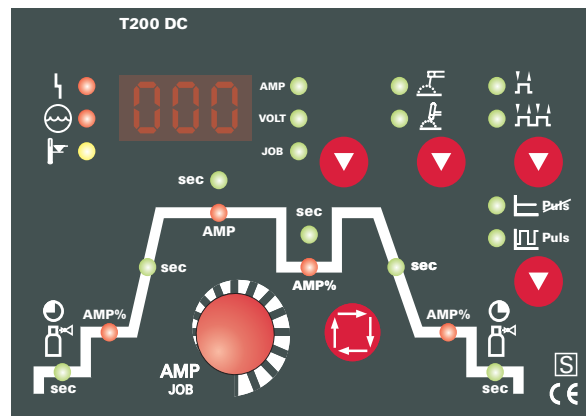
Устройство управления инверторного источника тока EWM для сварки ВИГ TRITON 220 DC PowerSinus
